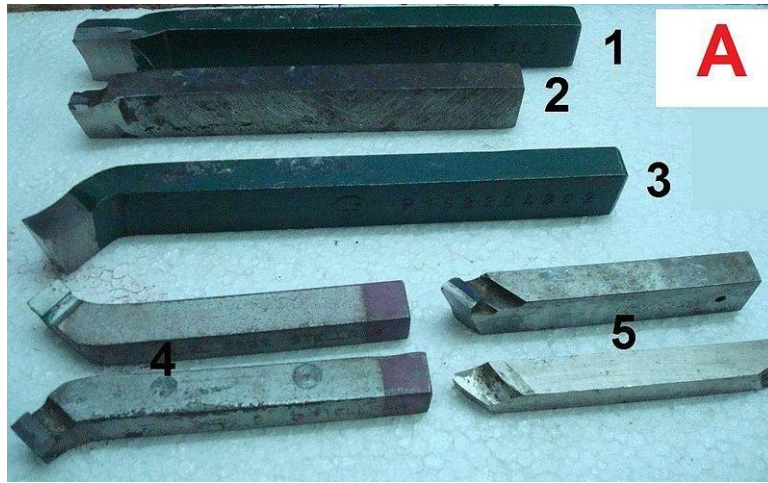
SÉRIE D'OUTILS POUR USINAGE EXTERNE
